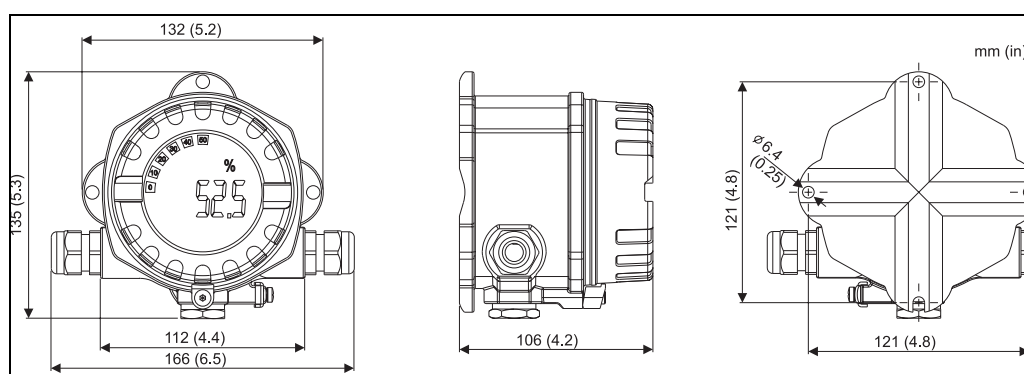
Dimensiones para la instalación; indicadas en mm (en pulgadas entre paréntesis)
